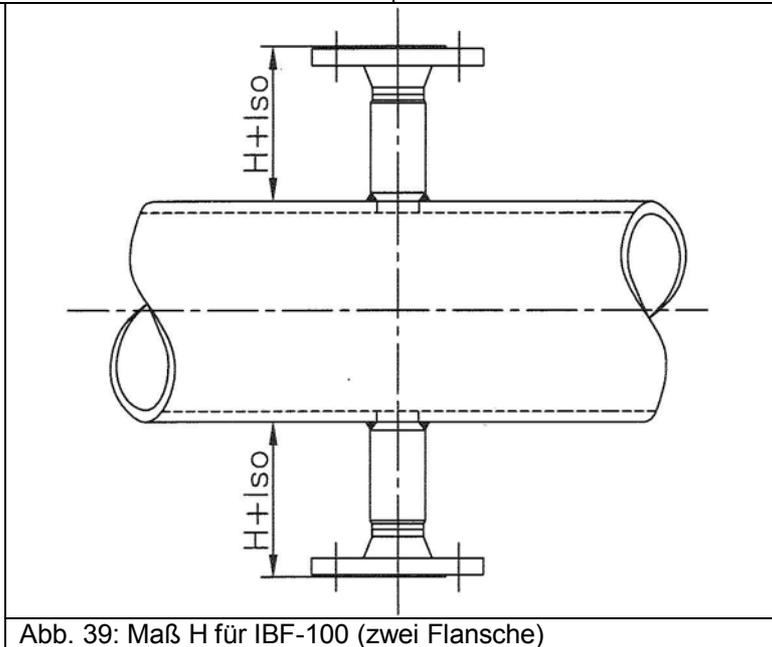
Maß H für IBF-100 (zwei Flansche)
